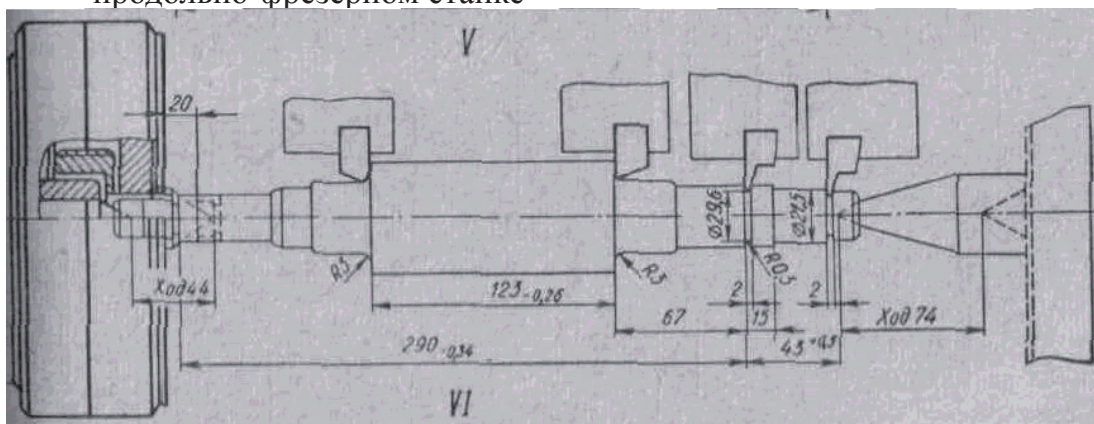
Схема одновременной токарной обработки поверхностей ступенчатого вала
